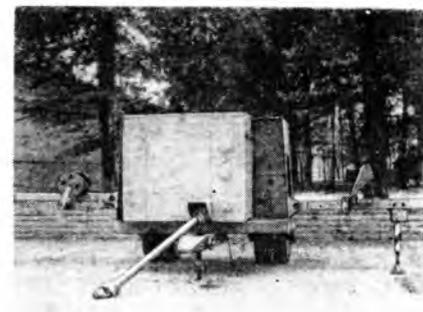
Роторный окорочный станок КГ-02 (ВНР)
